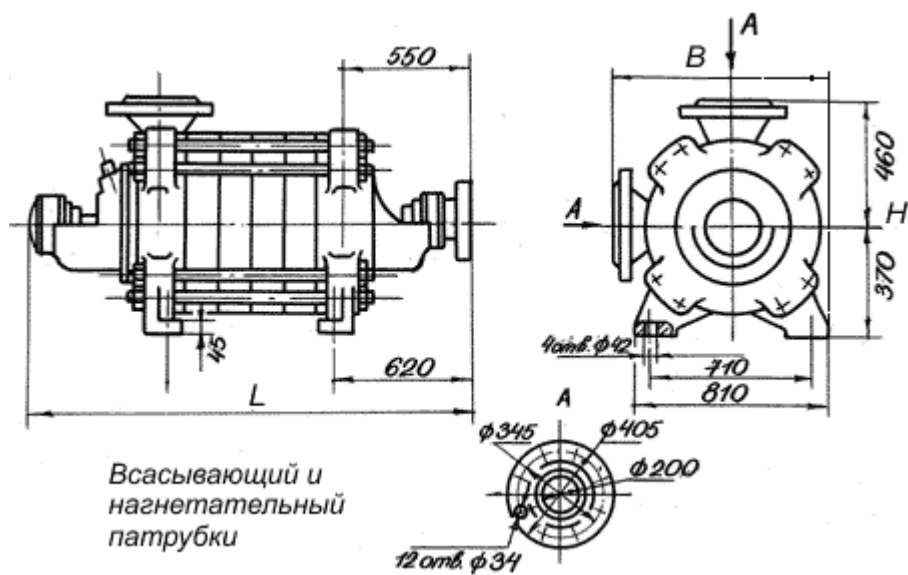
Габаритный чертёж насоса ЦНС 300-300.
